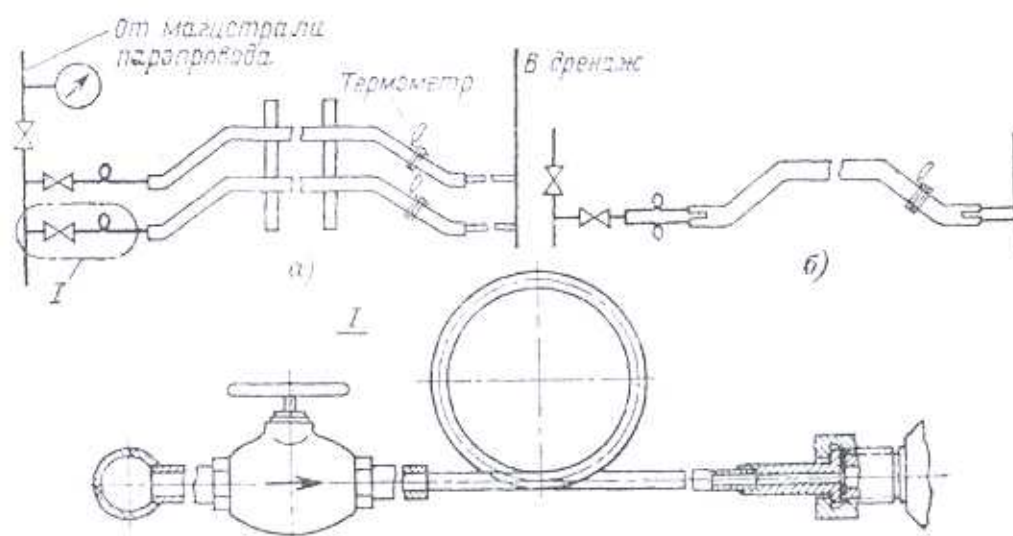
Приспособление для прогрева паром стержней статора при укладке обмотки
